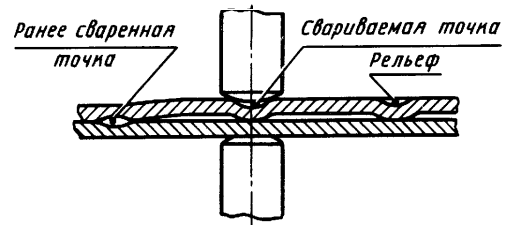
Схема рельефно-точечной сварки горячекатаной стали
